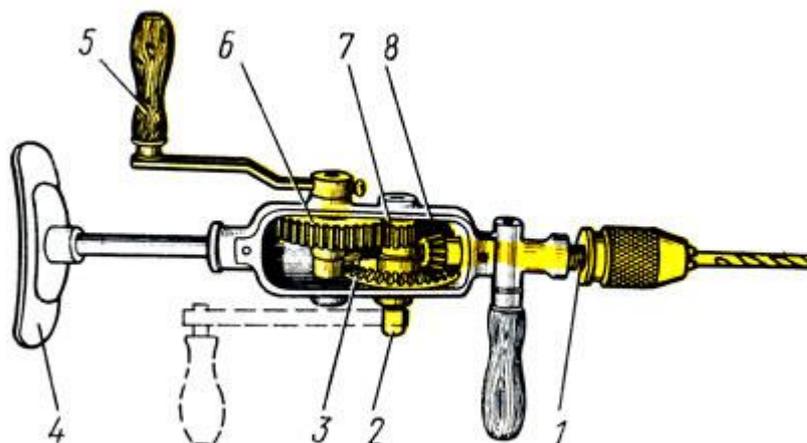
Ручная дрель: 1 - шпиндель, 2 - вал, 3, 6, 7, 8 - зубчатые колеса, 4 - упор, 5 - рукоятка
